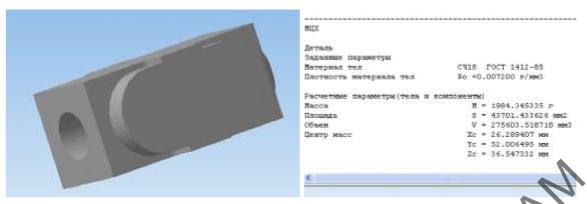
Визначення маси заготовки для лиття за виплавними моделями
